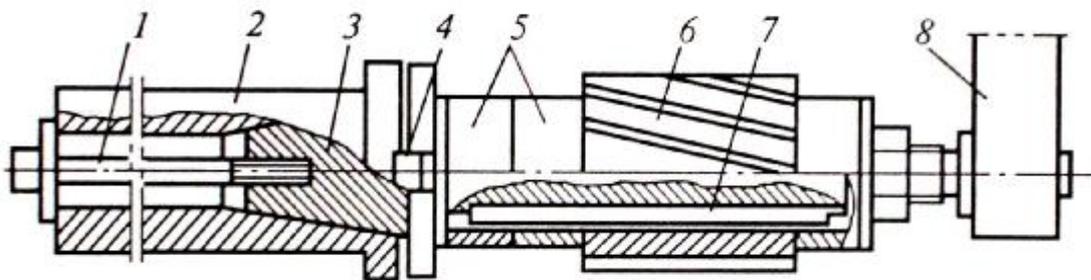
Установка цилиндрической фрезы на длинной оправке: 1 – шомпол; 2 – шпиндель; 3 – оправка; 4 – сухарь; 5 – проставочные кольца; 6 – фреза; 7 – шпонка; 8 – подвеска [1]
